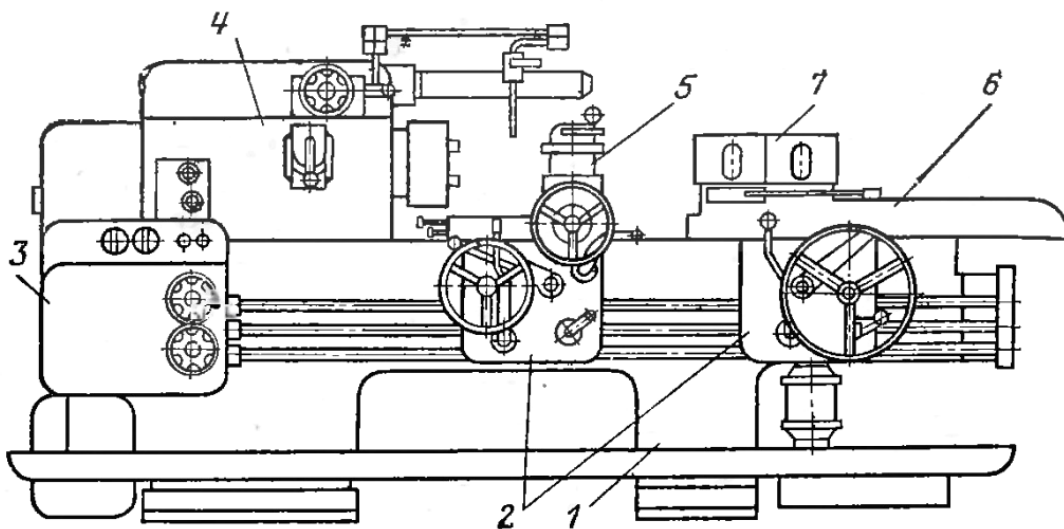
Загальний вигляд токарно-револьверного верстата моделі 1П365
